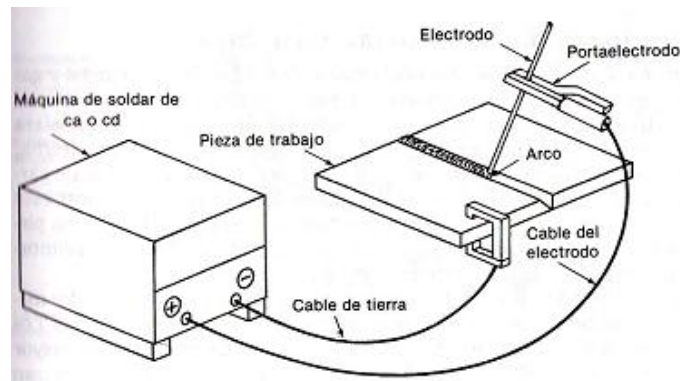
Disposición de elementos básicos para soldadura de arco metálico protegido.
